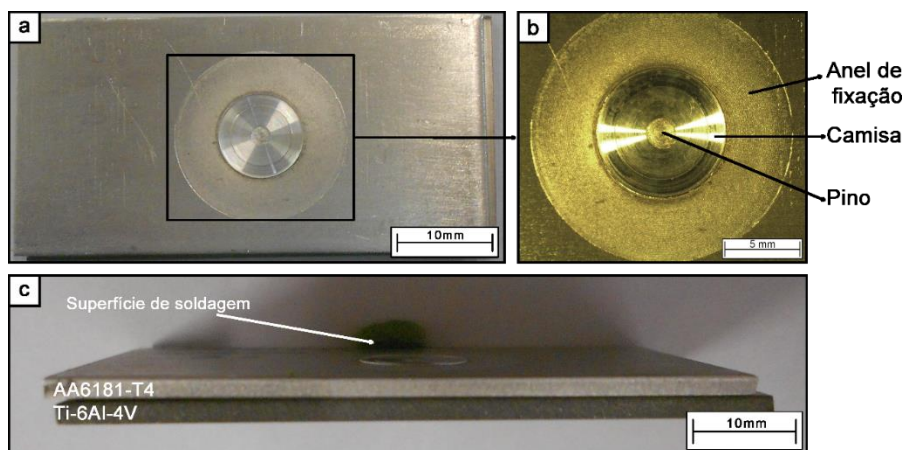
Junta AA6181-T4/Ti-6Al-4V como recebida: (a) topo da solda; (b) detalhe da região soldada; (c) imagem transversal da junta soldada.
